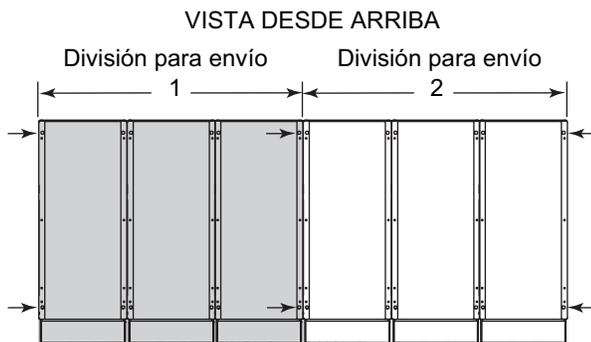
Unión de las separación para el transporte e instalación de los paneles de extremo
